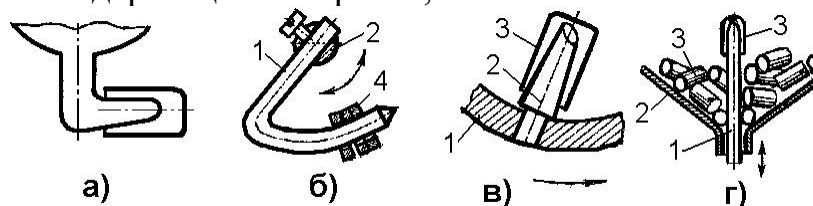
Конструктивные исполнения крючковых и штыревых захватно-подающих механизмов
